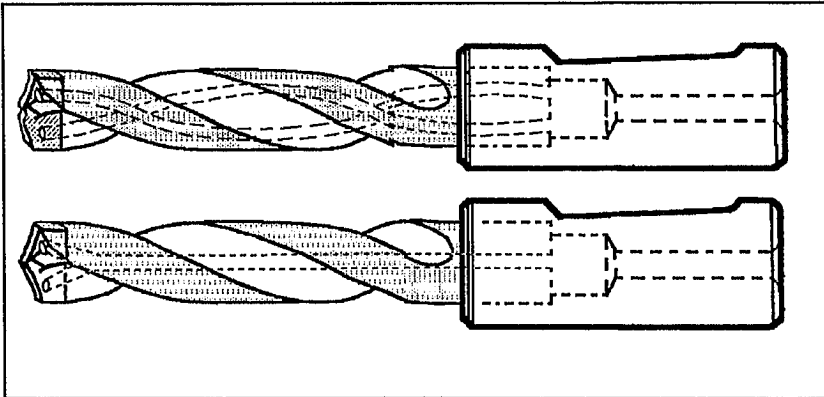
Um hohe Temperaturen an den Schneiden von Zerspanungswerkzeugen zu verringern, besteht die Möglichkeit, mit Kühlkanälen durch das Werkzeug das Kühlmittel an die Schneiden zu bringen. Dabei wird unterschieden zwischen verdrallter und zentraler Kühlmittelzufuhr. Gleichzeitig fördert das Kühlmittel den Spanablauf.
